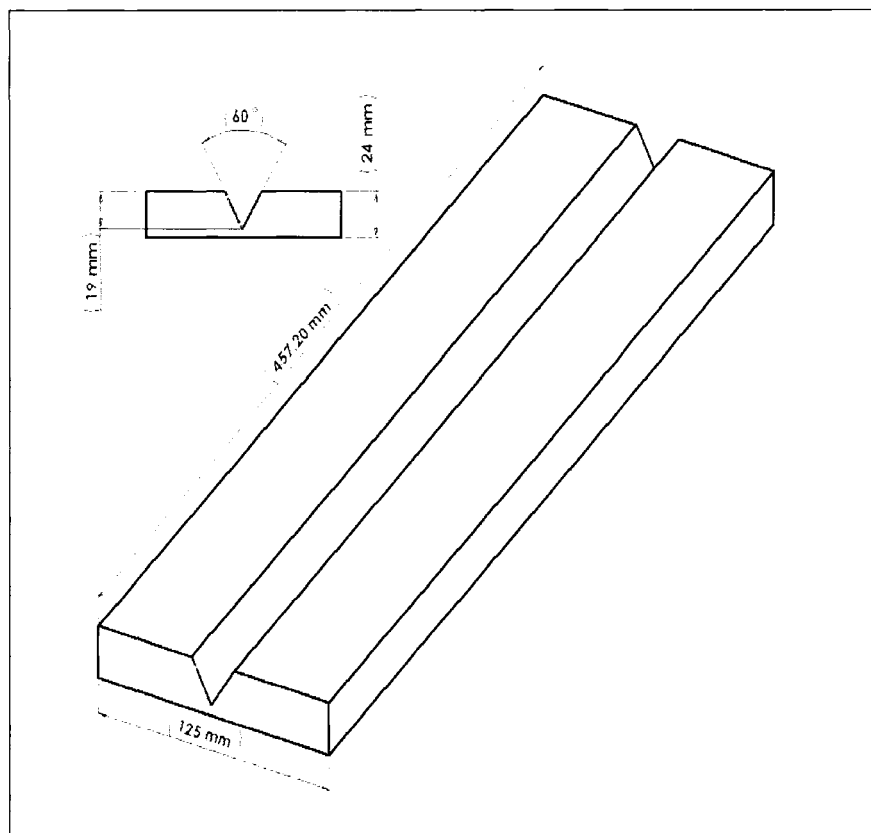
Préparation avant soudage de la plaque en acier A516.
